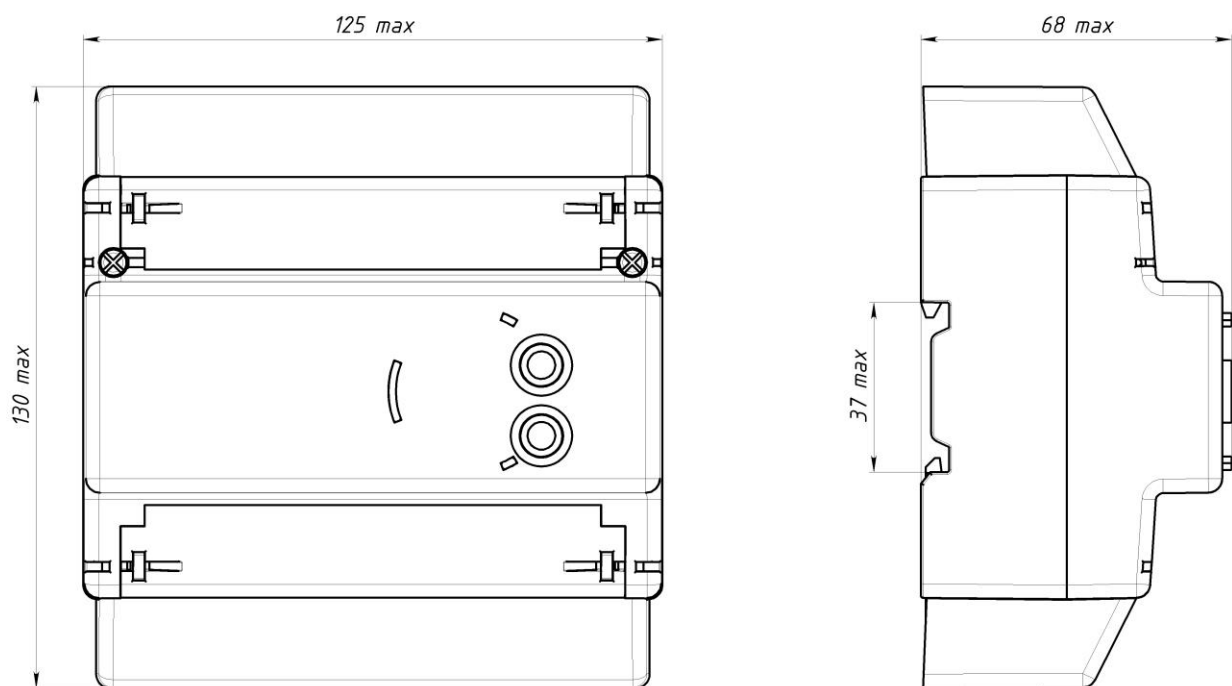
Корпус 7мТН35 со стандартными клеммными крышками
